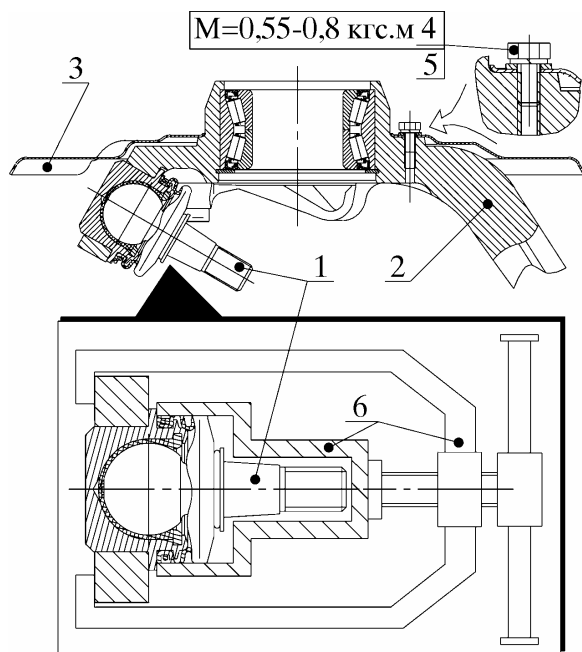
Запрессовка нижнего шарнира в отверстие поворотной стойки левой (правой) и установка щита тормоза: 1 - нижний шарнир, дет. 3111-2904314; 2 - поворотная стойка; 3 - щит, дет. 3111-3501015 (3111-3501014), тормоза; 4 - болты; 5 - шайбы пружинные; 6 - приспособление
